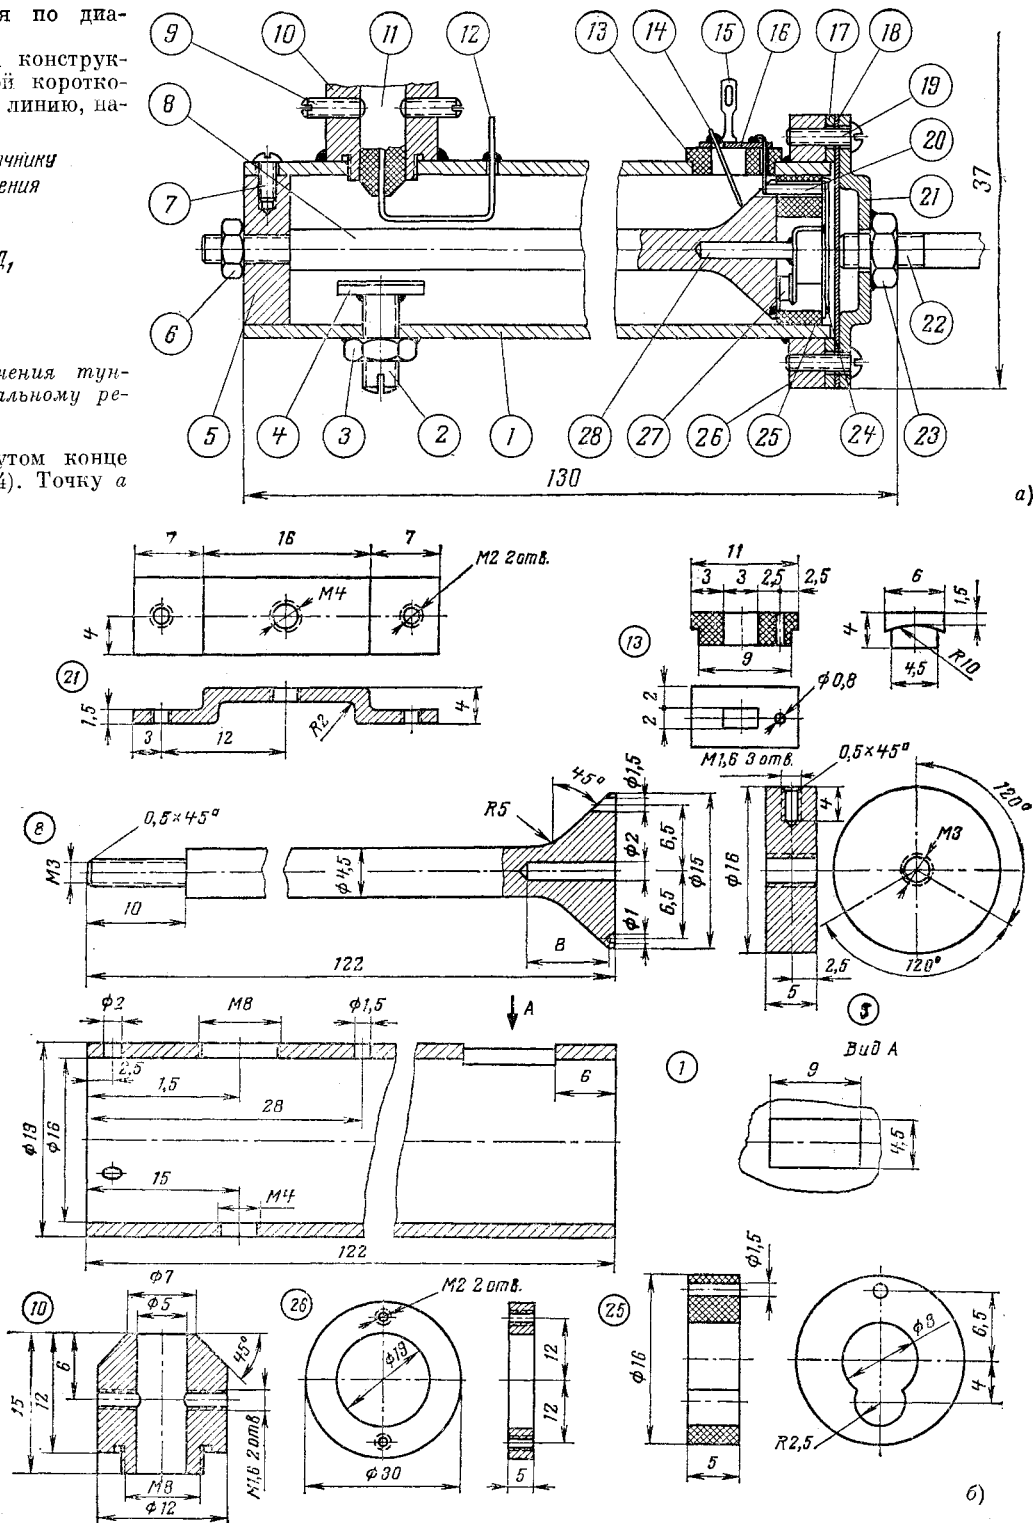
а — сборочный чертеж, б — детали резонатора.
